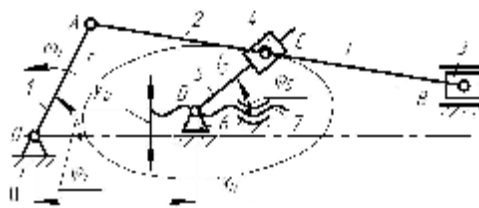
Двокривошипний шестиланковий важільний механізм з регульованою міжосьовою відстанню
